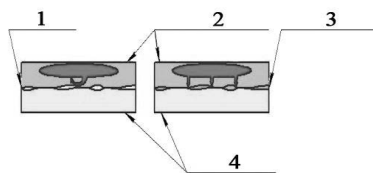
Приклад опорних поверхонь ріжучої пластини та інструментальної державки:
